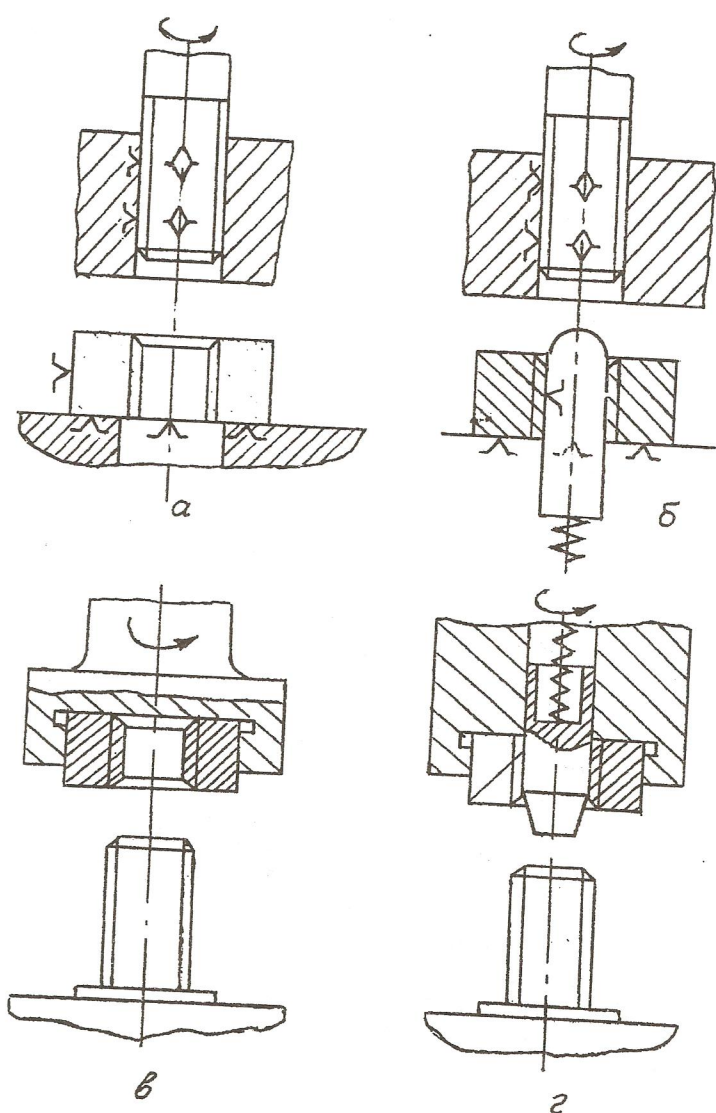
Схемы базирования резьбовых деталей: а - винт - на наружную поверхность, гайка - на торец; б - винт - на наружную поверхность, гайка центрируется по внутренней; в - винт неподвижен, гайка базируется на торец и наружную поверхность; г - винт неподвижен, гайка базируется на торец и внутреннюю резьбовую поверхность
